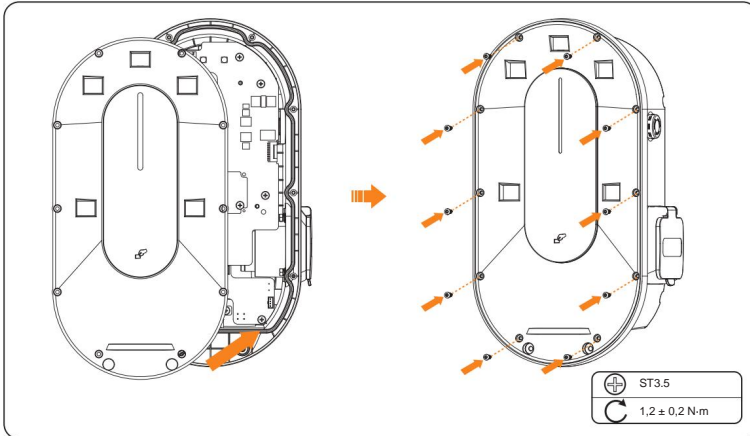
Frontplattenabdeckung wieder anbringen
